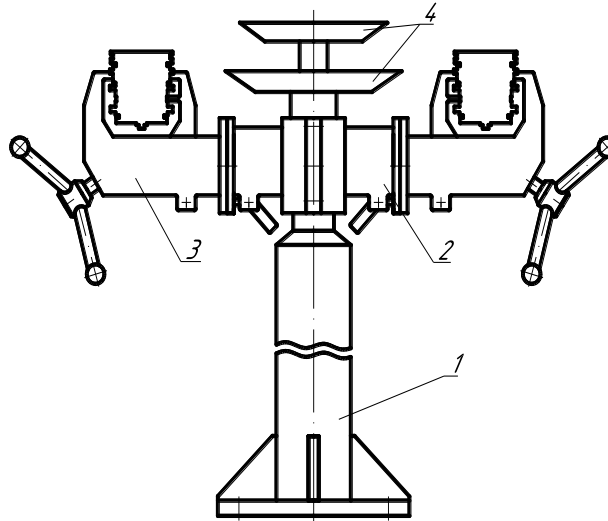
Стенд для ремонту коробок передач моделі 2218: 1 – опора; 2 – супорт; 3 – захват; 4 – стелаж [4].
